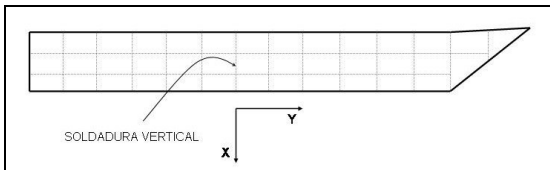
Esquema del casco de la barcaza donde se muestran las placas y la disposición de las juntas soldadas.
